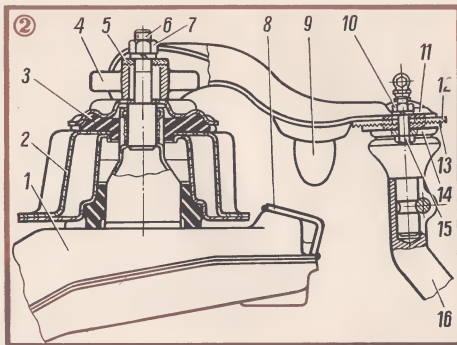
Установка верхнего рычага с измененным креплением оси и шарового шарнира: 1 — поперечина; 2 — лонжерон рамы; 3 — верхняя подушка; 4 — ось верхнего рычага; 5 — зубчатая накладка; 6 — шпилька поперечины; 7 — гайка; 8 — угольник; 9 — буфер отбоя; 10 — гайка крепления; 11 — верхний рычаг; 12 — зубчатая пластина, приваренная к рычагу; 13 — зубчатая пластина шарового шарнира; 14 — шаровой шарнир; 15 — стальной болт; 16 — поворотная стойка.
